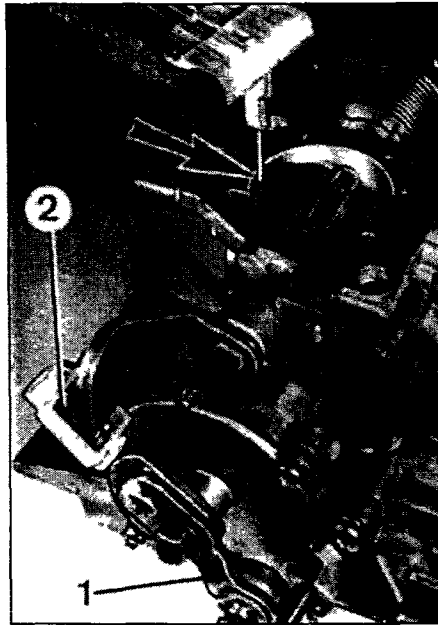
Регулировка пусковых оборотов - карбюратор снят
